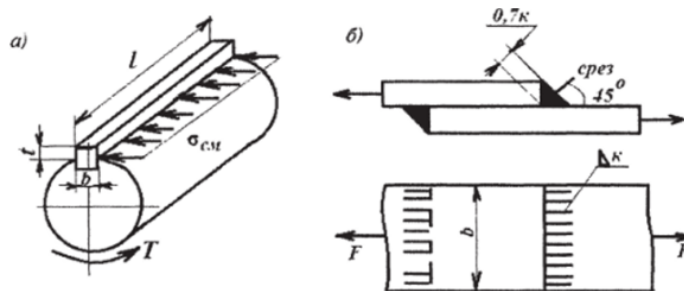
Соединения: а) шпоночное; б) сварное
